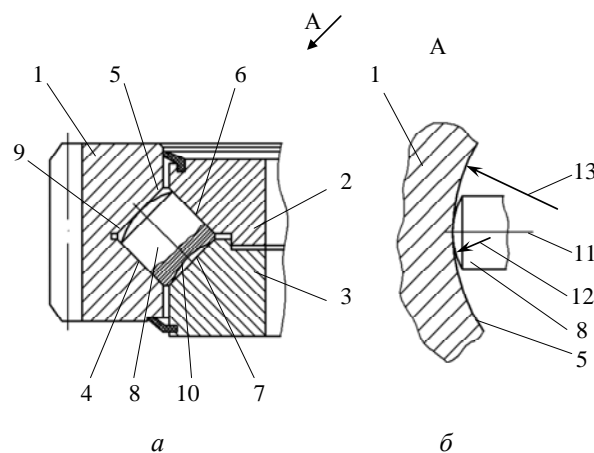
Принципова конструкція опорно-поворотного пристрою з модифікованими роликами:
